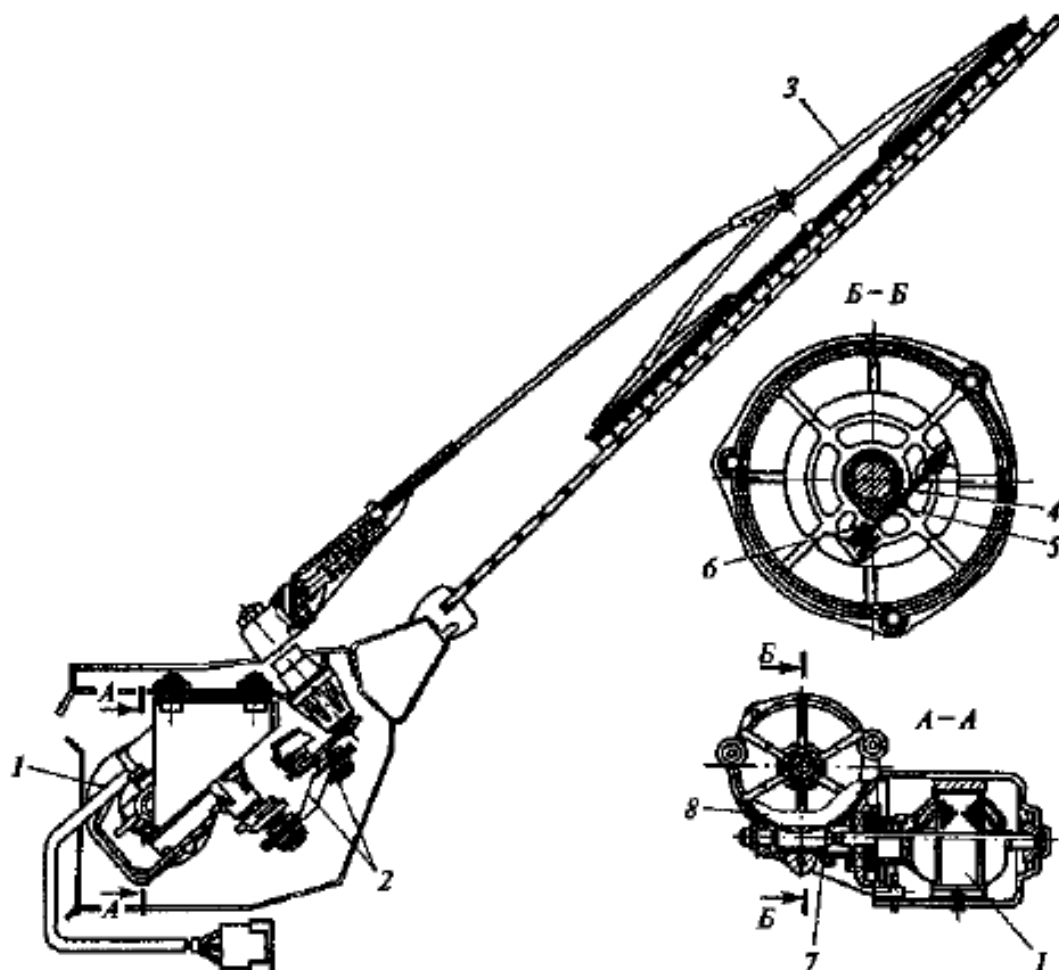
Типовой электрический стеклоочиститель: 1 – электродвигатель; 2 – рычаги; 3 – щетка; 4 – эксцентрик; 5 и 6 – контакты (подвижный и неподвижный); 7 – червячный вал; 8 – шестерня
